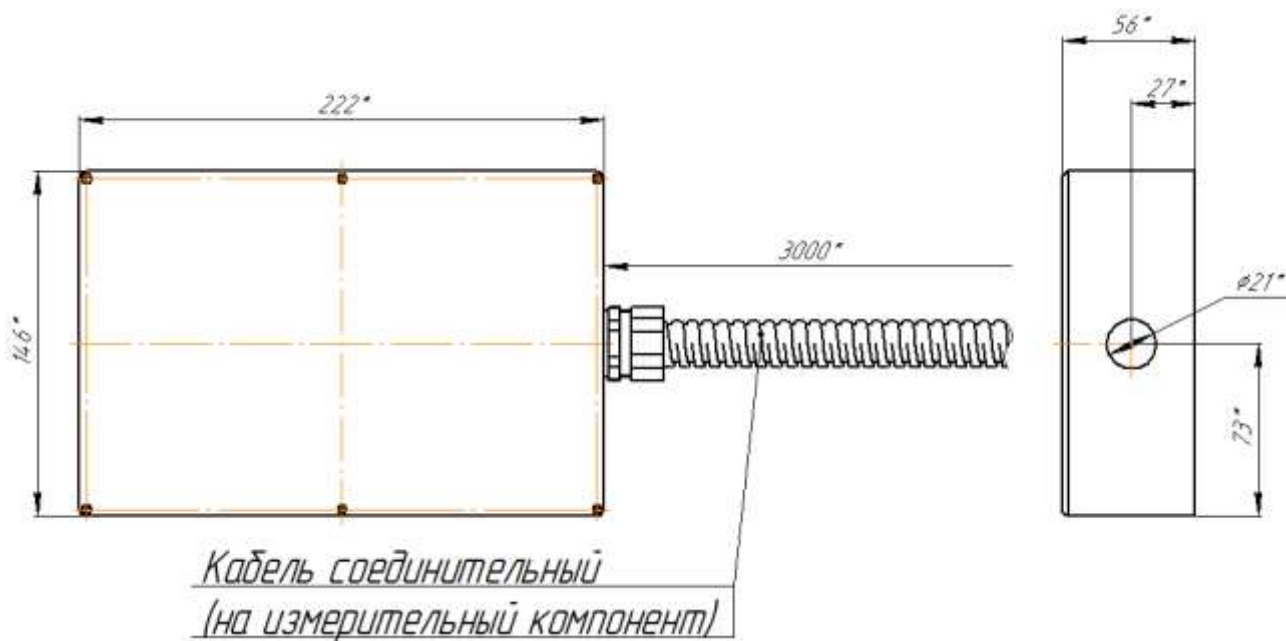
Ж – габаритно-установочные размеры коробки соединительной.
